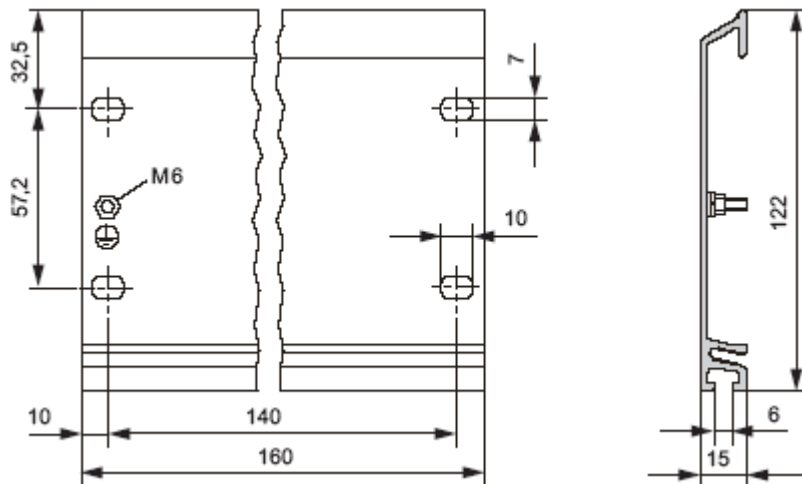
Габаритный чертеж профильной шины стандартной ширины 160 мм.
